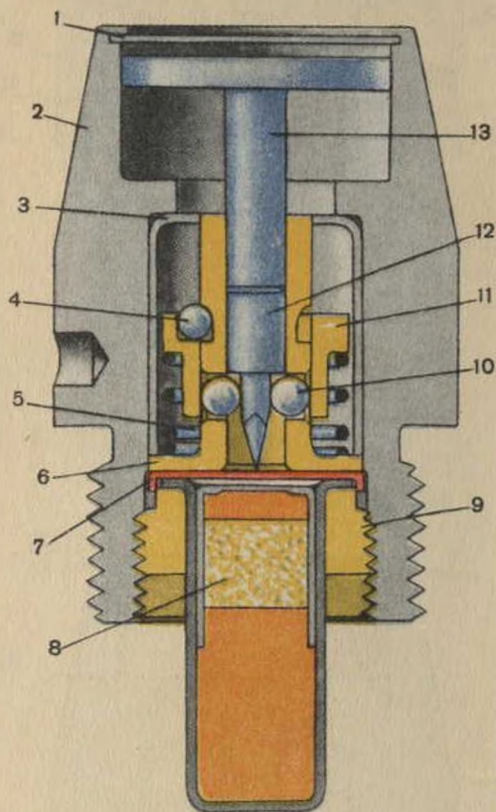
Взрыватель БМ (в разрезе): Положение деталей взрывателя до выстрела:
